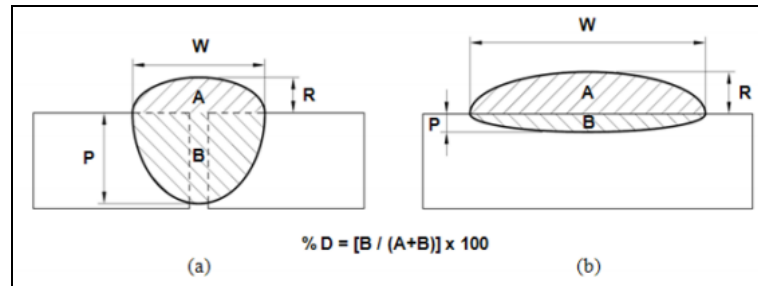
Perfil geométrico do cordão de solda: a) soldagem de penetração (aplicação convencional); b) soldagem de revestimento. Fonte: (GOMES, 2010, p. 10)
